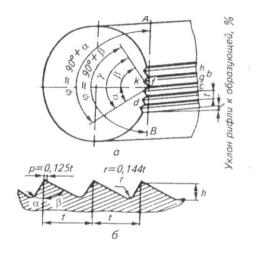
Форма (а) и профиль рифлей (б) вальцового станка
